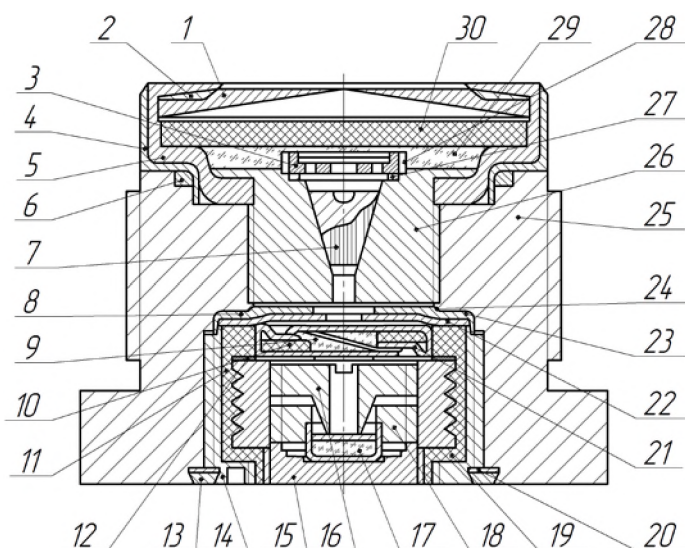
Втулка ГУВ-7: 1 – крышка обтюлятора; 2 – герметизирующая прокладка; 3 – заделка; 4 – манжета; 5 – обтюратор; 6 – прокладка; 7 – обтюрирующий конус; 8 – мостик накаливания; 9 – воспламенительный состав; 10 – пергаментный кружок; 11 – электроизолирующая колодка; 12 – латунный кружок; 13 – поджимное кольцо; 14 – зажимная втулка; 15 – основание; 16 – наковаленка; 17 – капсуль-воспламенитель; 18 – гайка; 19 – изолирующий слой; 20 – герметизирующая прокладка; 21 – нижний контакт; 22 – крышка; 23 – стальной кружок; 24 – верхний контакт; 25 – корпус; 26 – винт; 27 – кольцо; 28 – бумажный кружок; 29 – подсыпка дымного пороха; 30 – пороховая петарда
